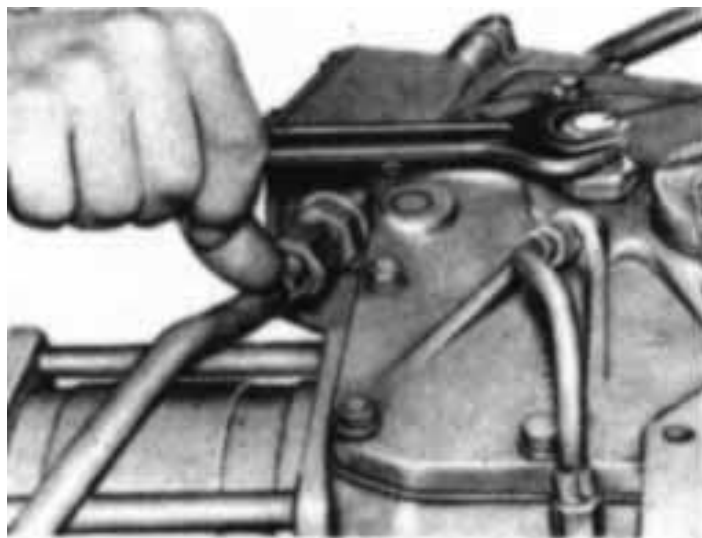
Регулювання вертикального переміщення поворотного валу.
